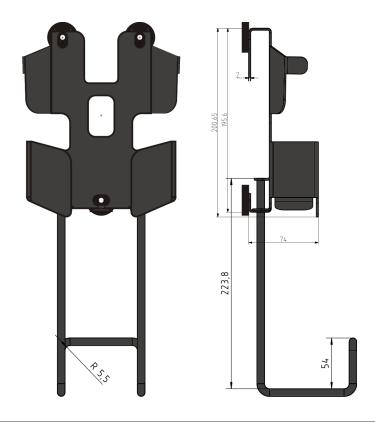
Rück- und Seitenansicht der Wandhalterung KeTop WB025 / WB026, (Maßangaben in mm)
